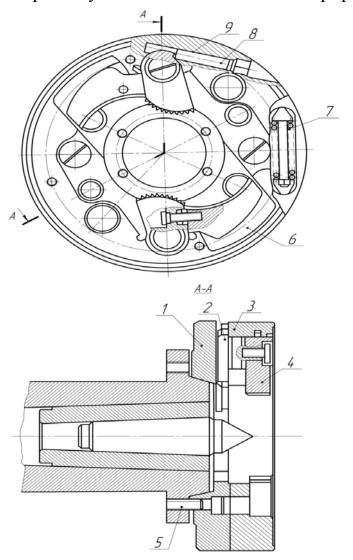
Поводковый центробежный патрон с двумя эксцентричными кулачками: 1 — фланец; 2 — ведущий палец; 3 — корпус; 4 — кулачок; 5 — винт; 6 — груз; 7, 8 — пружины; 9 — толкатель
